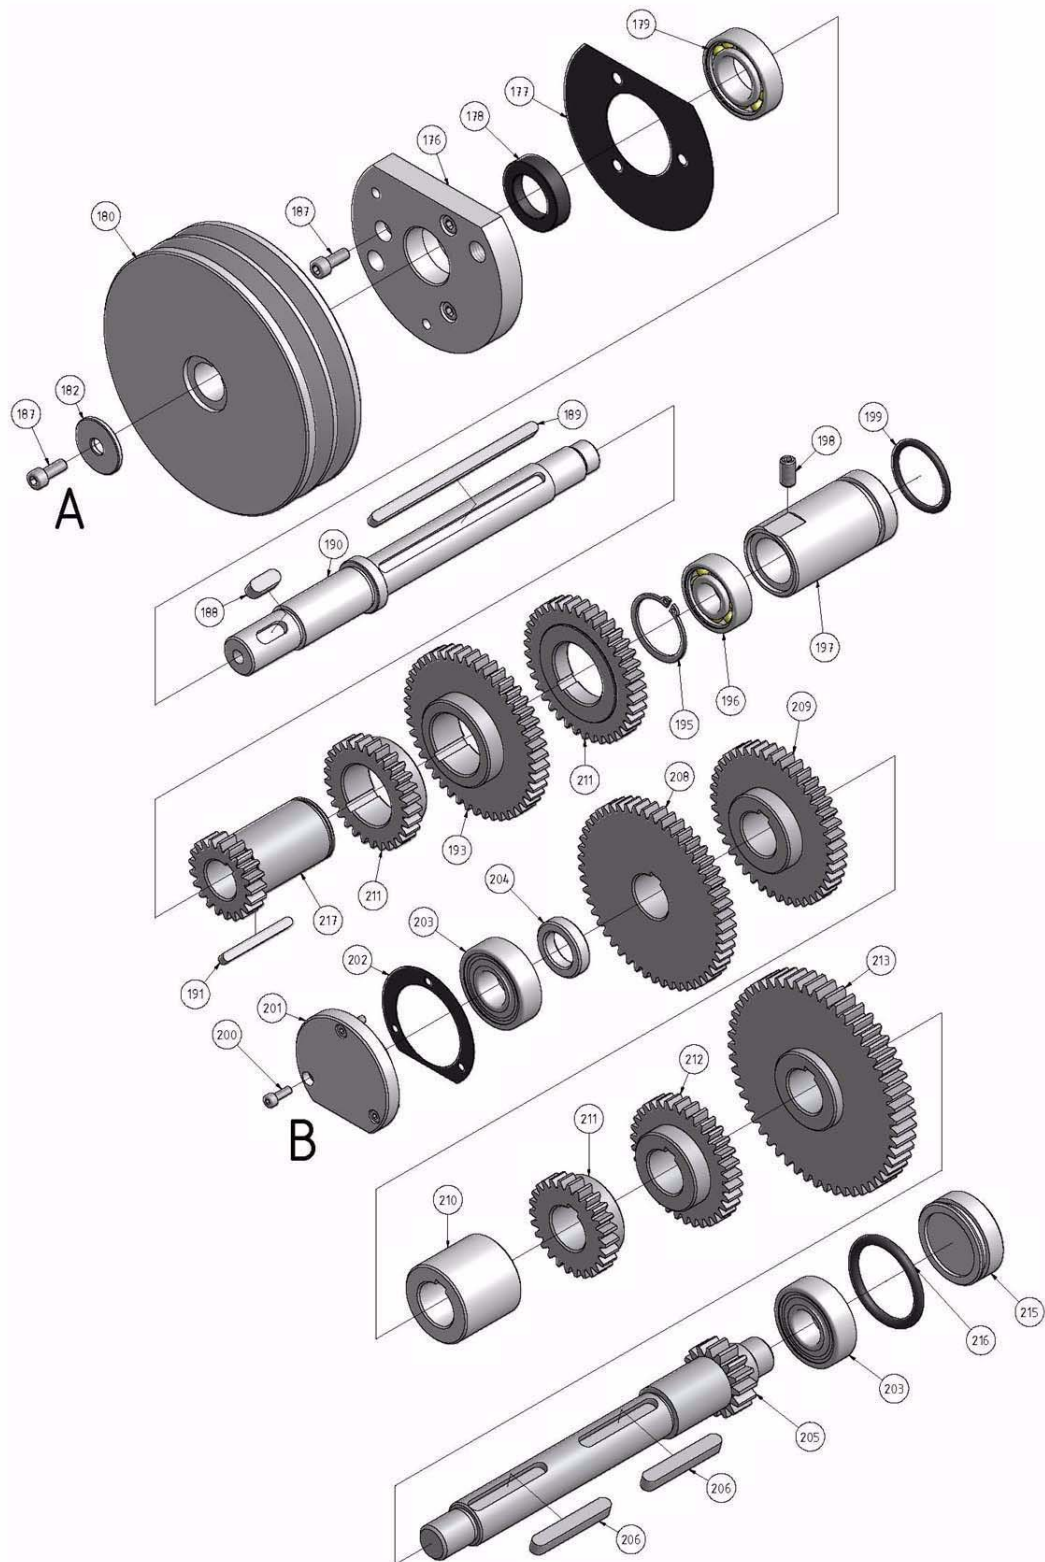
Getriebe Spindelstock 3-6 - Headstock gear 3-6
